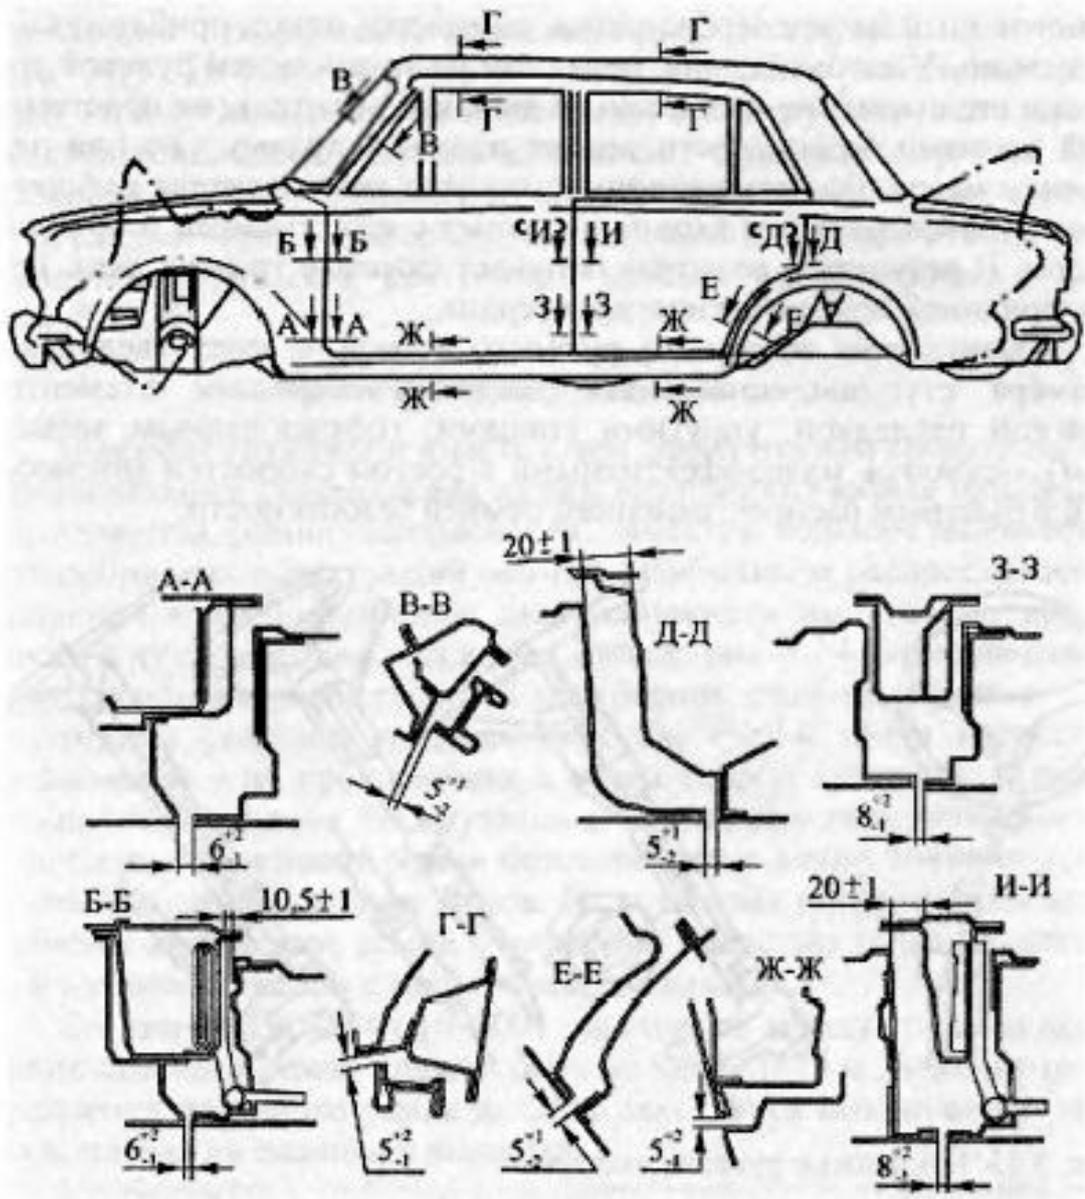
Схема деформации и основные сечения кузова ВАЗ-2101
